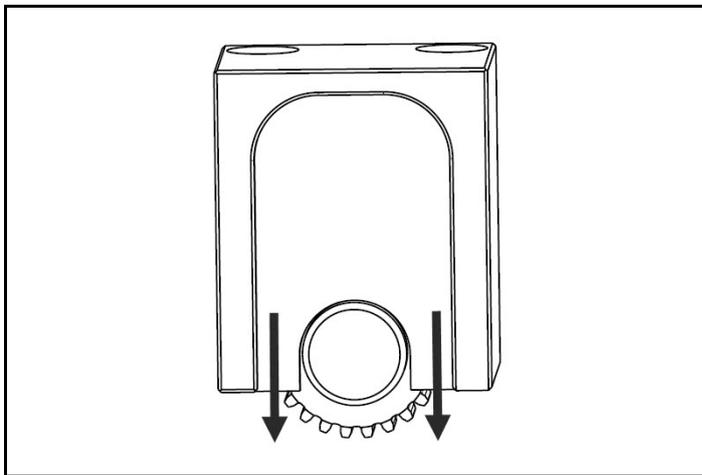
Retirer le couvercle de la boîte d'engrenages
